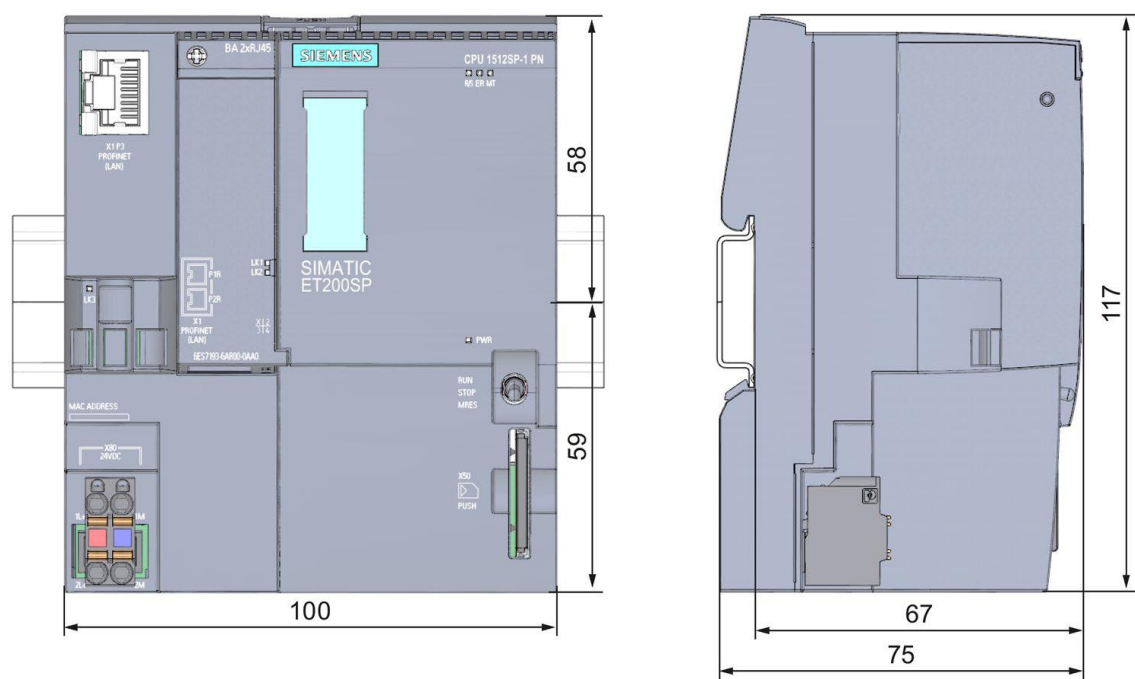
Габаритный чертеж CPU 1512SP-1 PN
